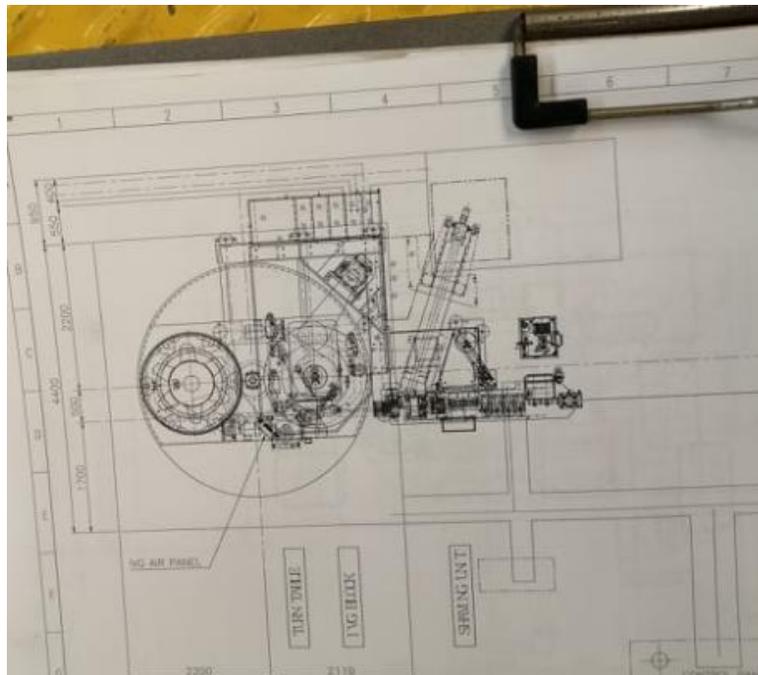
Vista alzada de maquina 2. Enrollador y pulidor
